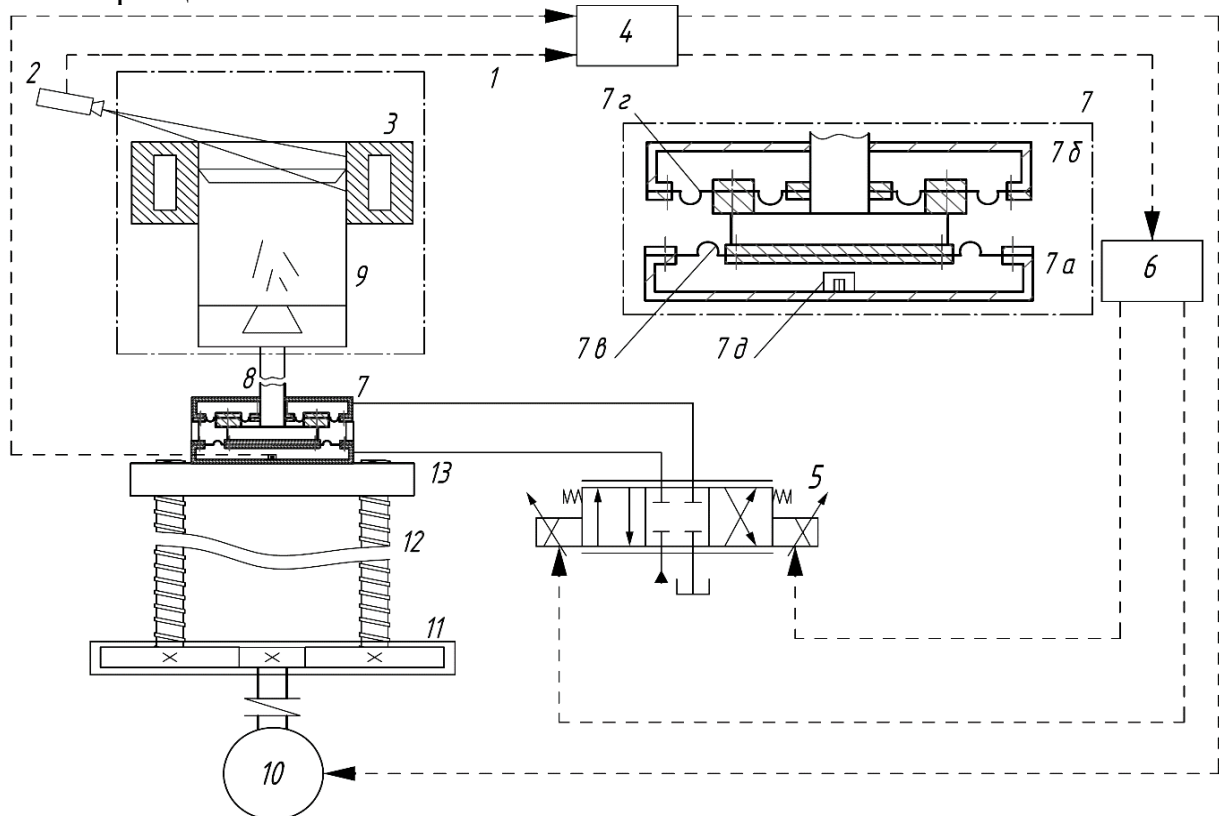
Контур керування витягуванням зливку з кристалізатора. 1 – плавильна камера; 2 – відеокамера рівня розплаву; 3 – кристалізатор; 4 – блок керування; 5 – електромагніти; 6 – блок керування електромагнітами; 7 – привод подачі коливань (7а,б – мембранні приводи, 7в та 7г – одно- та двоугофрова мембрани, 7д – датчик переміщення); 8 – шток; 9 – зливков; 10 – електродвигун; 11 – редуктор; 12 – гвинтова передача; 13 – платформа
